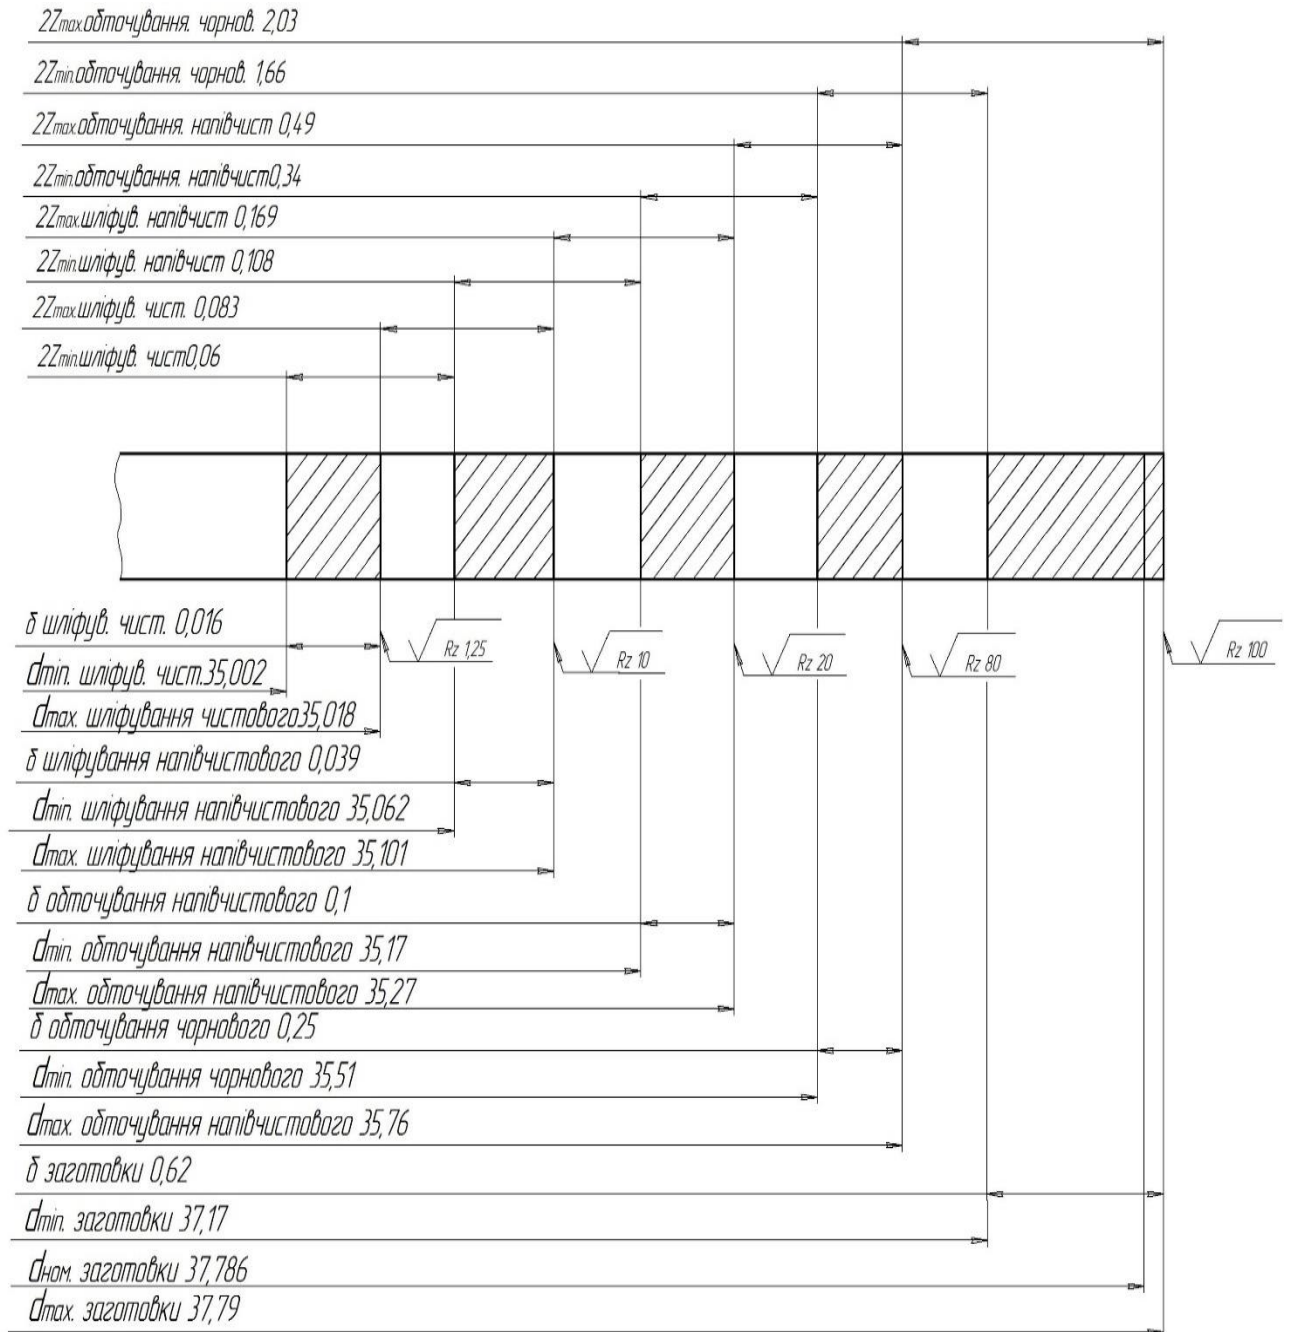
Схема графічного розташування припусків та допусків на обробку поверхні $\varnothing 35k6$.
